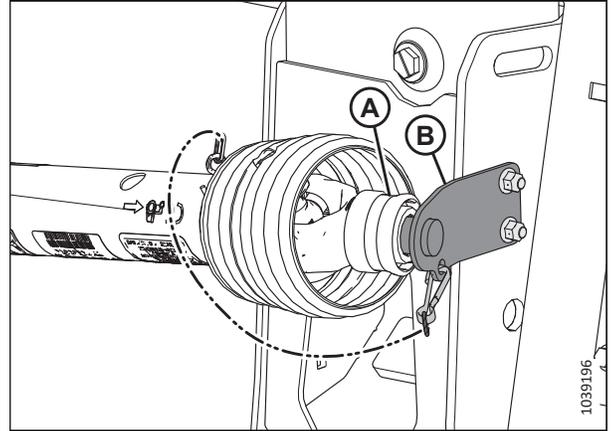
Prise de force en position de rangement – Prise de force B7038 ou B7039
